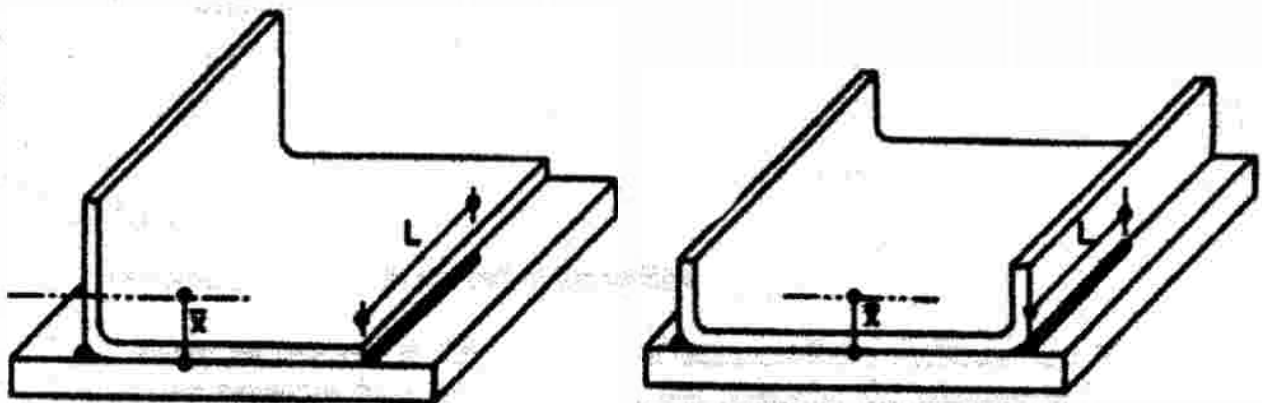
Definición de \bar{x} y L para soldaduras
